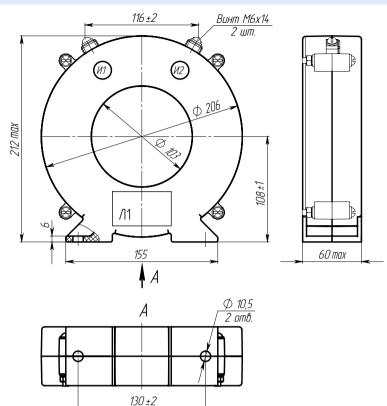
Общий вид трансформатора ТНШЛ-0,66 в пластмассовом корпусе на токи 600-2000 А
